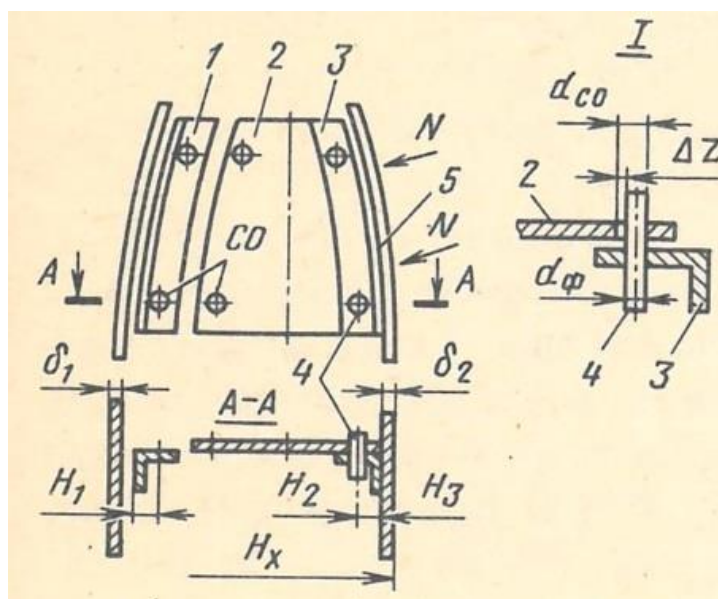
Схема базирования деталей по СО: 1, 3 – профили нервюры; 2 – стенка нервюры; 4 – фиксатор; 5 – обшивка; N – прижимающая сила.
